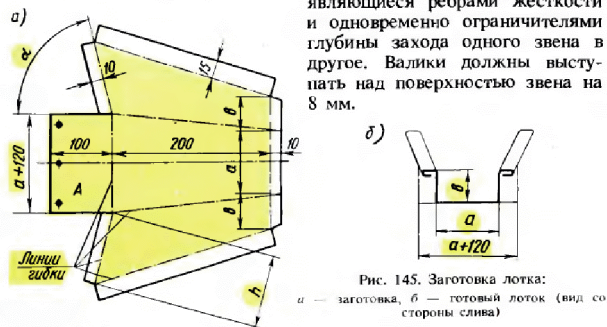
Заготовка лотка: а — заготовка, б — готовый лоток (вид со стороны слива)
